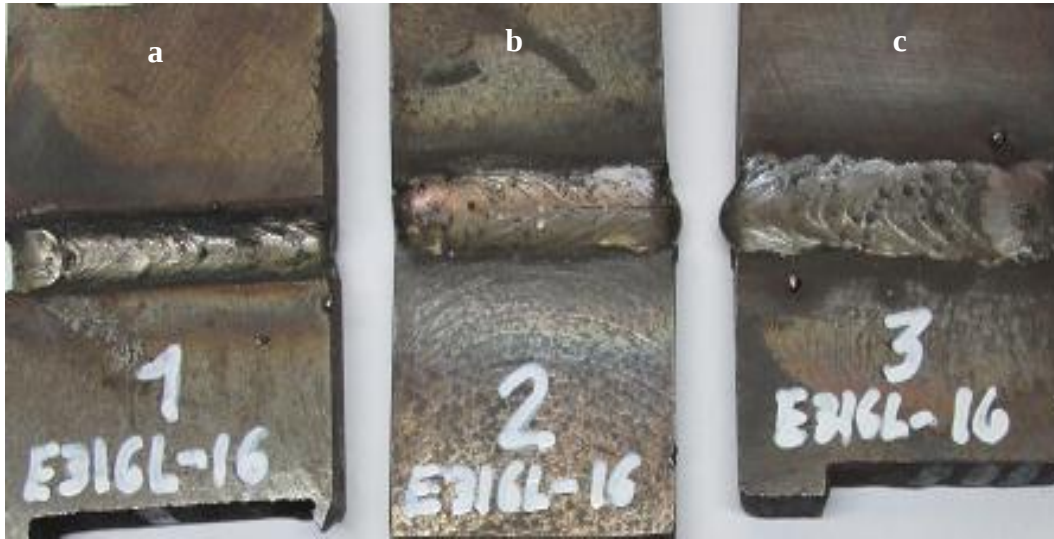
Muestras soldadas con electrodos E 316L - 16.
